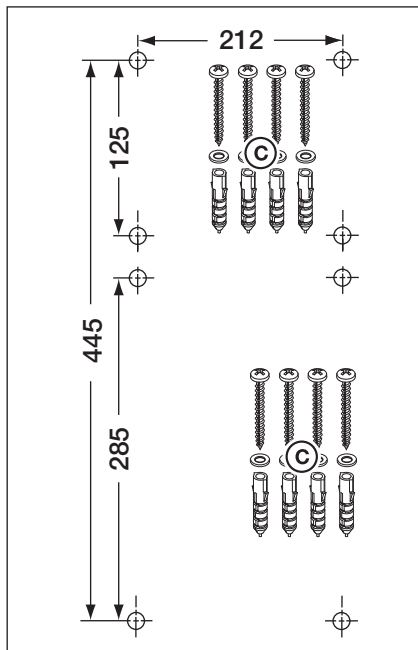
Схема расположения отверстий для крепления, необходимые детали для монтажа
